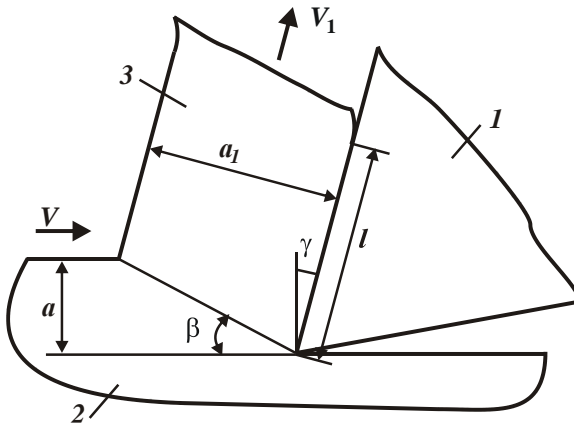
Розрахункова схема параметрів процесу стружкоутворення під час різання: 1 – різець; 2 – оброблюваний матеріал; 3 – стружка, що утворюється
